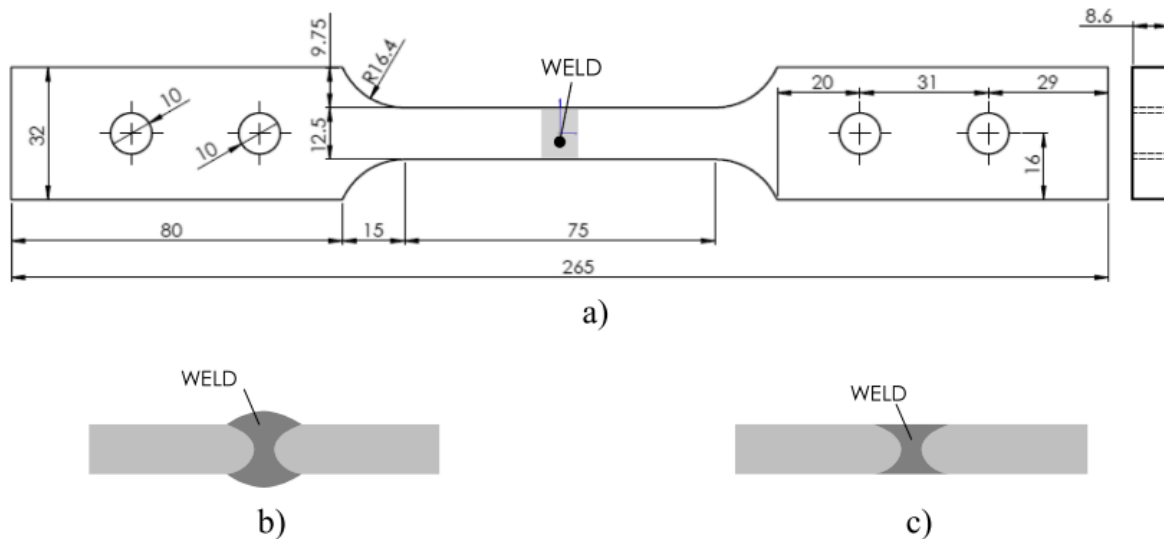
4 – a) Geometria e dimensões dos provetes de ensaio, b) Geometria de seção transversal como soldada; c) Geometria de seção transversal constante. (Fonte: D.M. Rodrigues et al.,2021)
